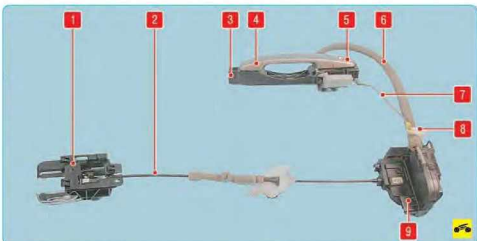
Привод замка передней двери: 1 – внутренняя ручка; 2, 6 – тросы привода замка; 3 – основание наружной ручки; 4 – наружная ручка; 5 – выключатель замка; 7 – тяга выключателя замка; 8 – рычаг выключателя замка; 9 – замок передней двери
